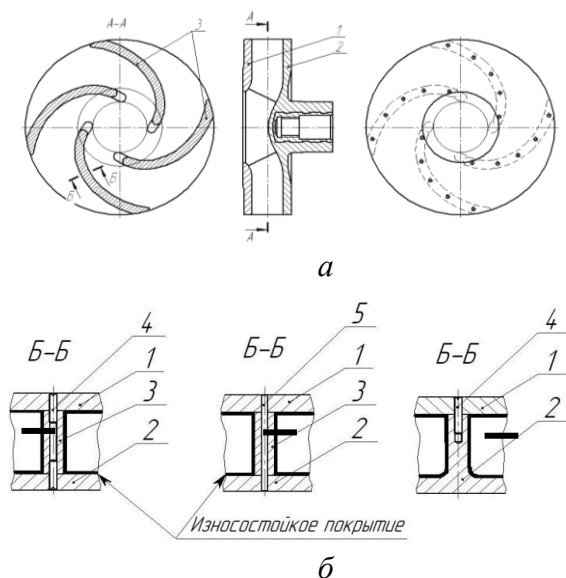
Сборное рабочее колесо насоса: а – рабочее колесо насоса; б – варианты выполнения сборочного колеса
